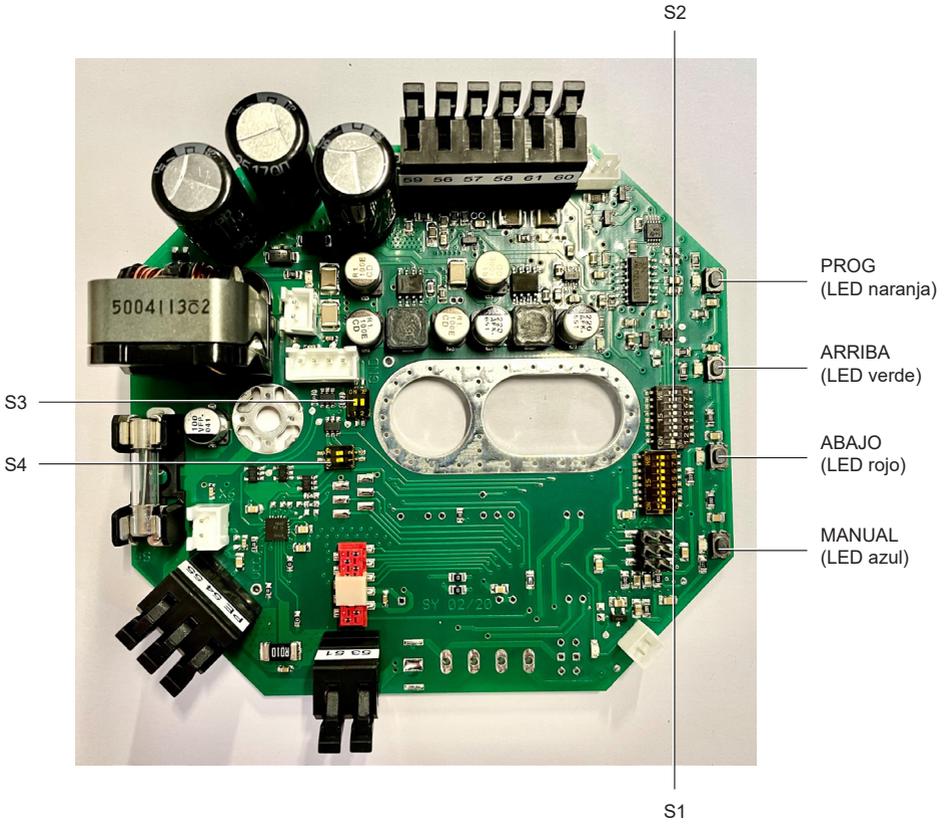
Tarjeta electrónica del posicionador Vcc (incluidas las versiones del módulo de desconexión)
